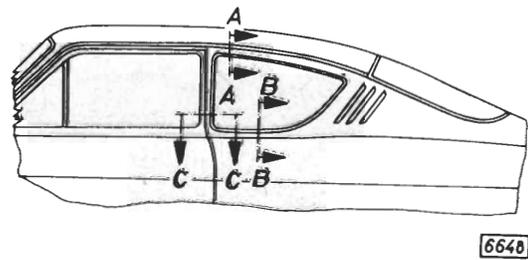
Anordnung der Schnitte für Befestigung Zierrahmen am Schwenkfenster - hier am Coupé gezeigt
